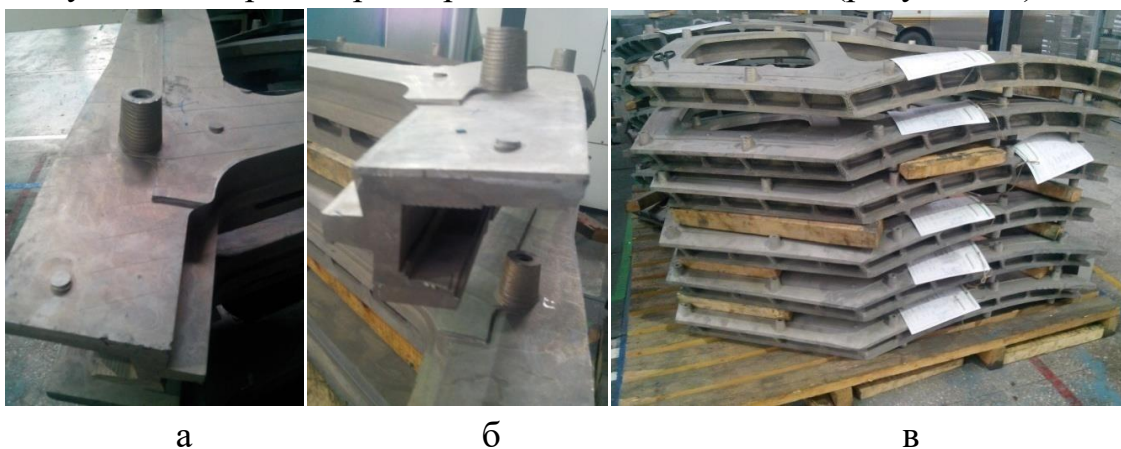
Общий вид заготовки рамы переплета фонаря с равномерным припуском 6 мм
